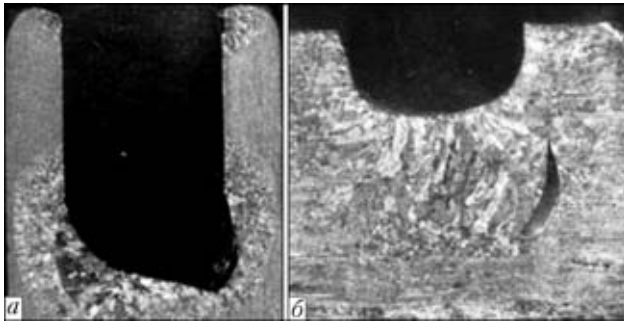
Поперечные макрошлифы закристаллизовавшихся швов: *а* — форма свободной поверхности сварочной ванны; *б* — несплавление, образовавшееся в результате исчезновения жидкой прослойки
